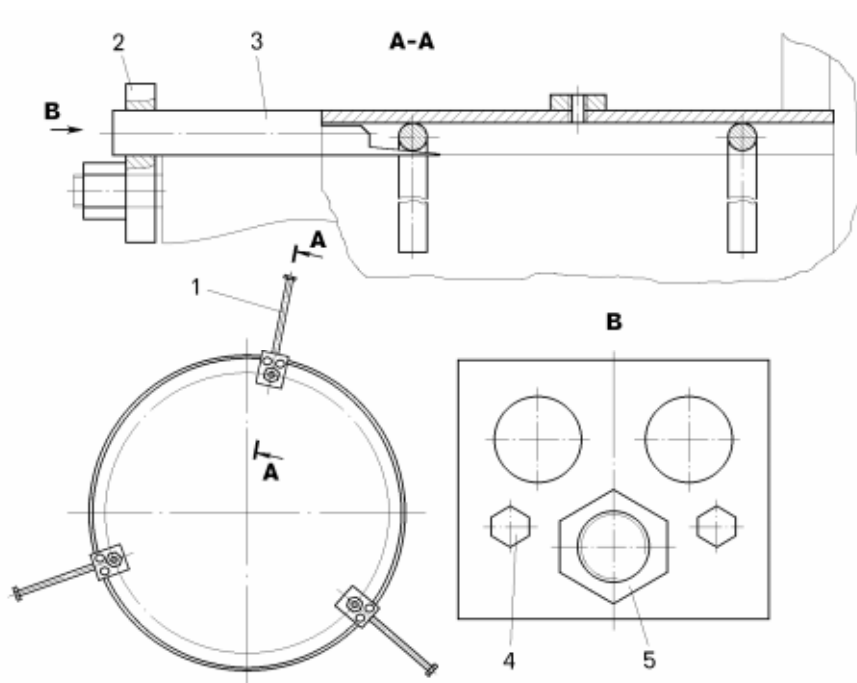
Приспособление для центровки внутреннего колеса с шиной на ступице:
